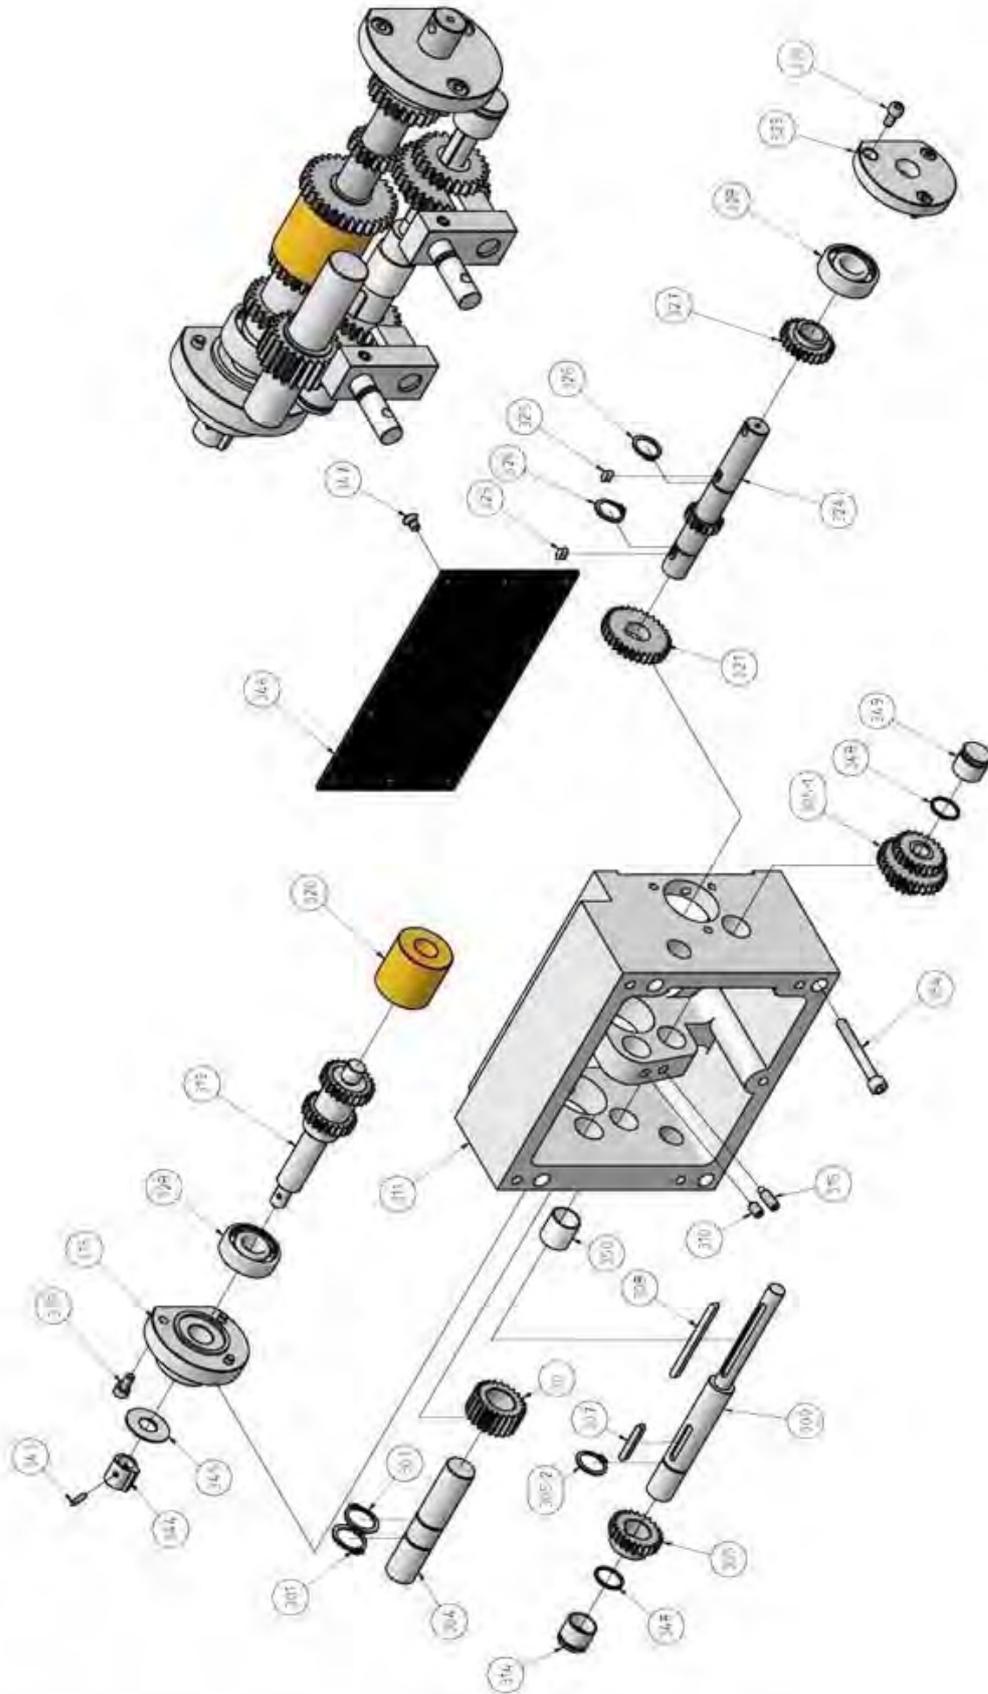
Vorschubgetriebe 2 von 2 - Engranajes de alimentación 2 de 2 - TU 2807
